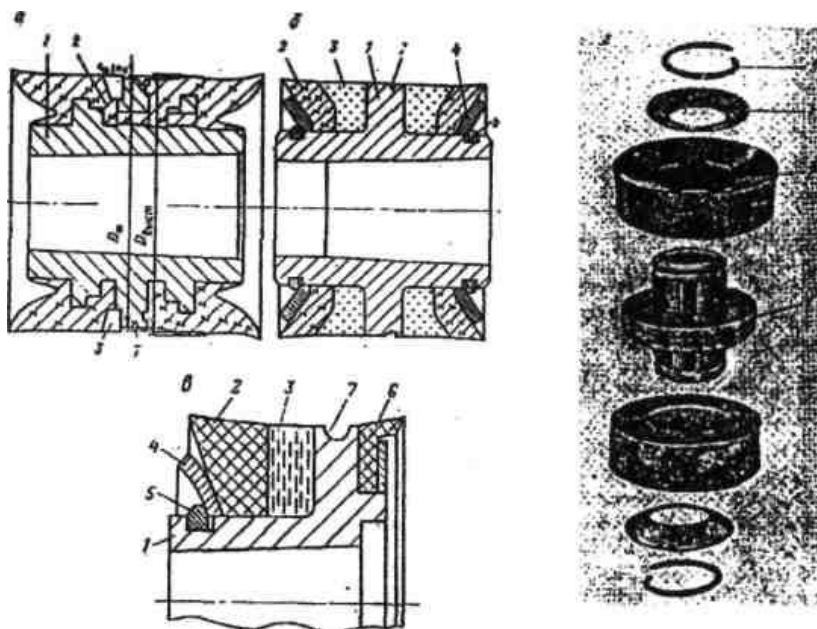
Поршни насосов: 1 - ступица; 2 - манжета поршня; 3 - кольцо- манжеты; 4 - шайба; 5 - запорное кольцо; 6 - очищающая манжета; 7 - контрольная проточка
